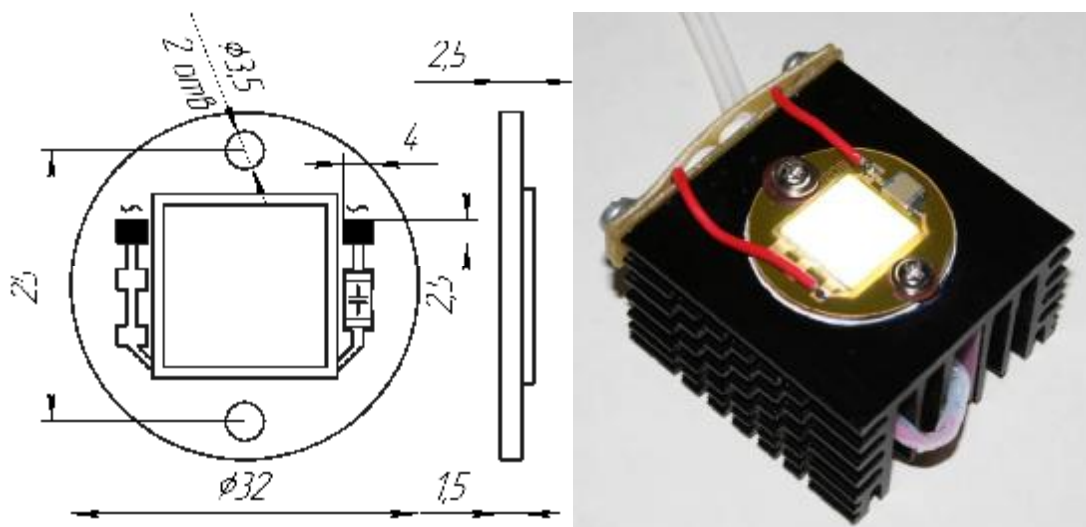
Габаритный чертеж и внешний вид СИМ-8Б-220
